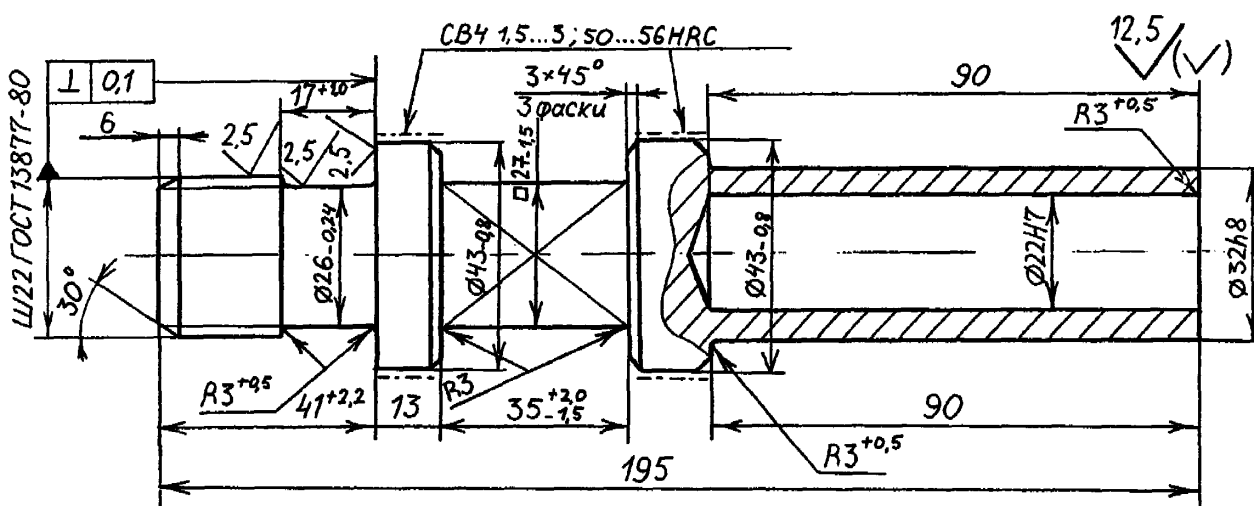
Конструкція головки склопластикової штанги $\varnothing 22$ мм
